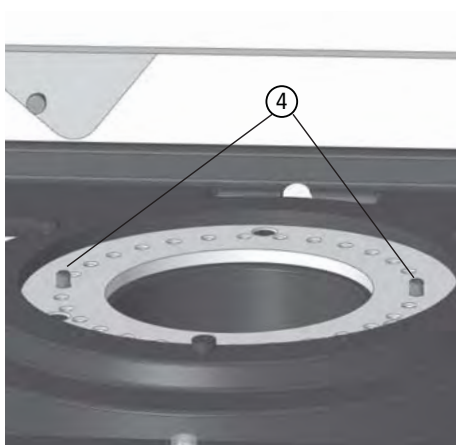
Tiges de butée, réglage des butées gauche et droite
